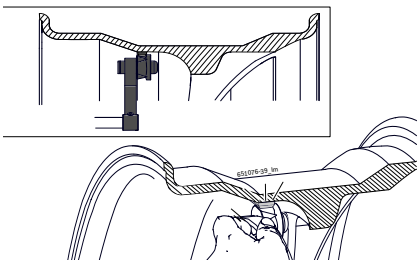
ALU3 - ALU2 - Klebegewicht auf 2. Auswuchtebene anbringen.
